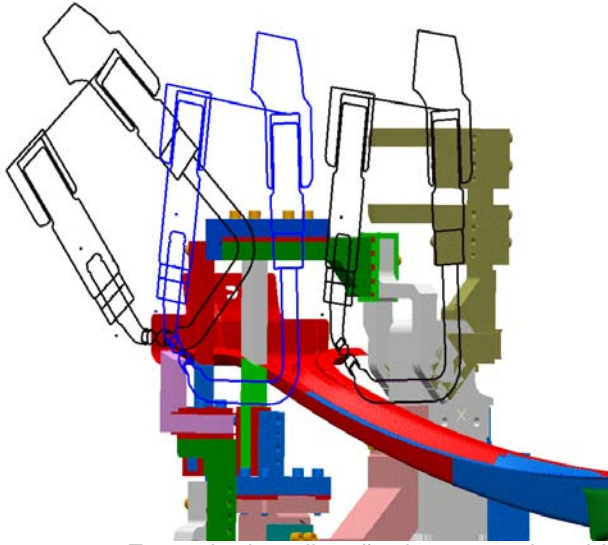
Exemplo de aplicação de pontos de solda.
